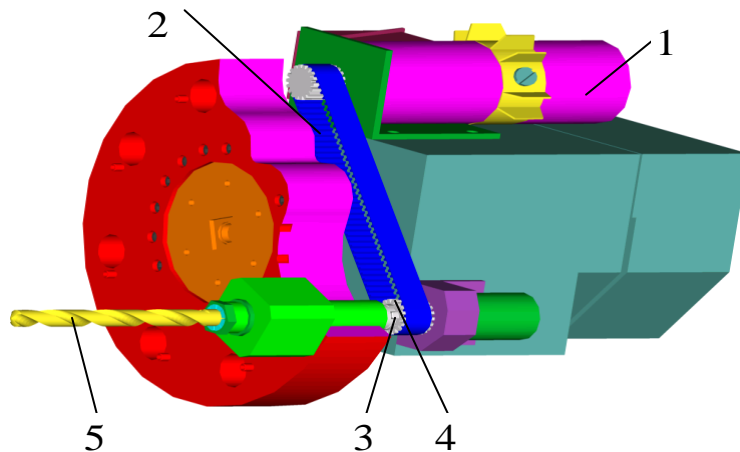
Схема шестипозиционной револьверной головки с вращающимся инструментом: 1 – приводной двигатель; 2 – зубчатая ременная передача; 3, 4 – полумуфты; 5 – инструмент
